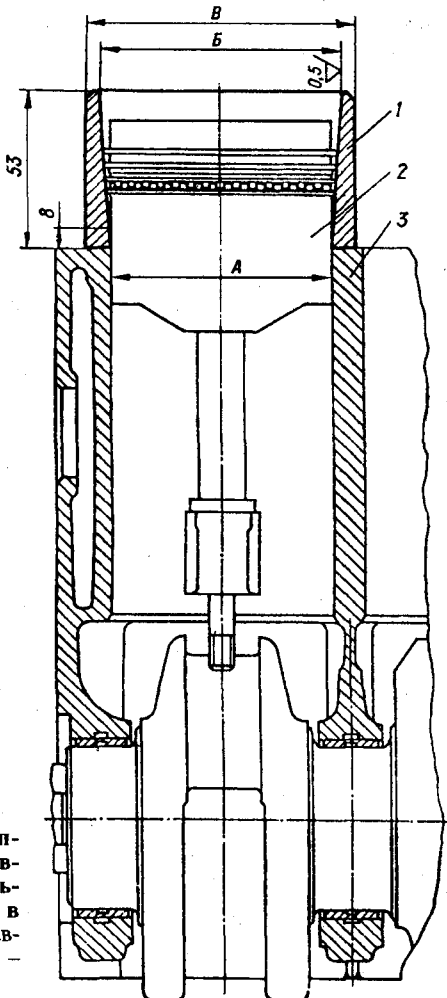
Оправка для установки поршня с кольцами и шатуном в цилиндр: 1 – оправка; 2 – поршни; 3 – блок
